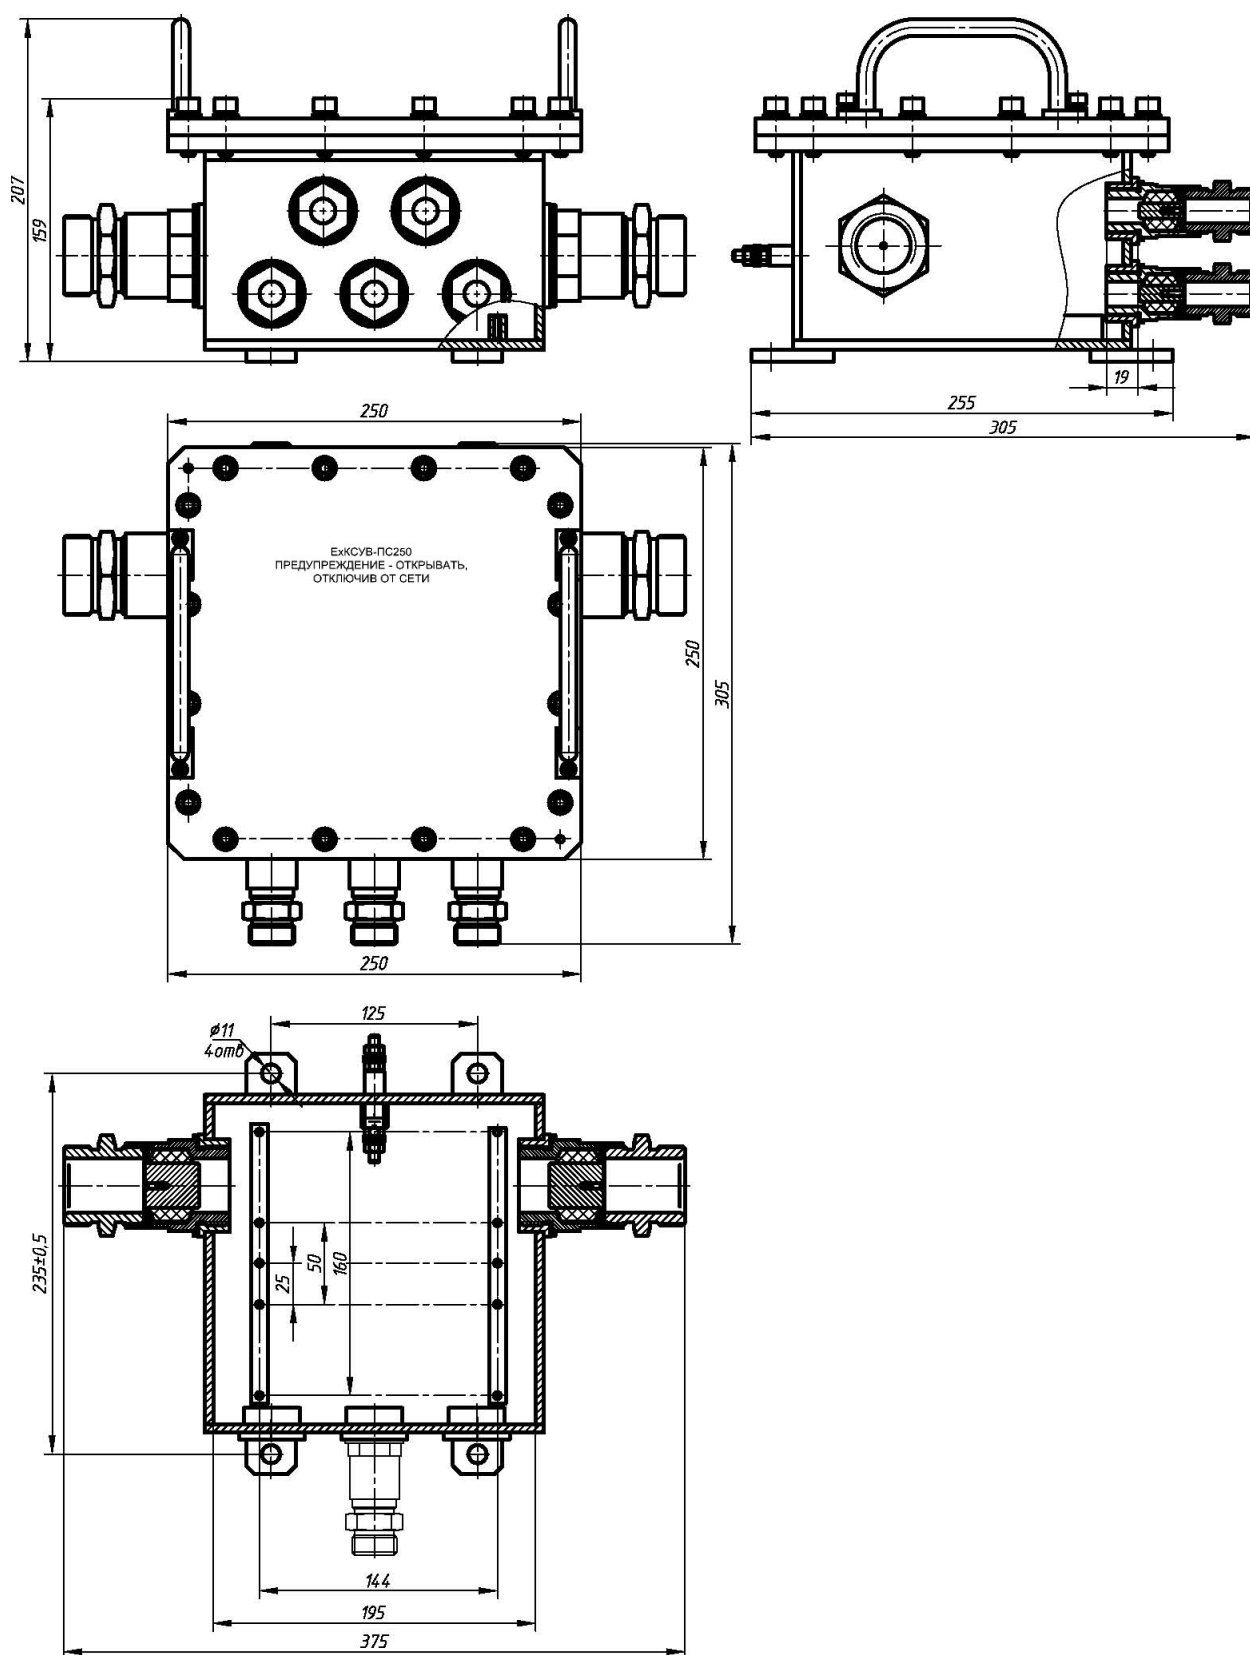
Габаритный чертеж коробки ЕхКСУВ-ПС250.
